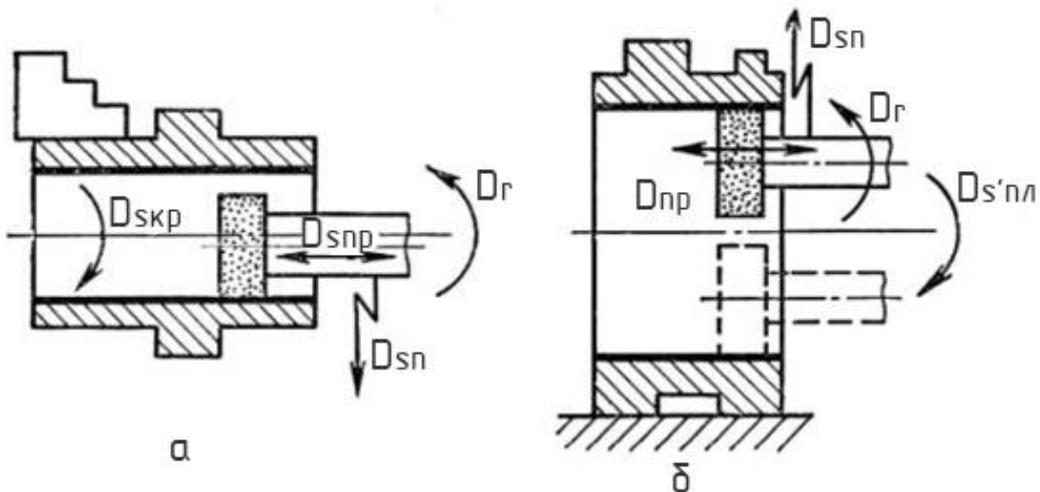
Схема обработки заготовки на внутришлифовальных станках
